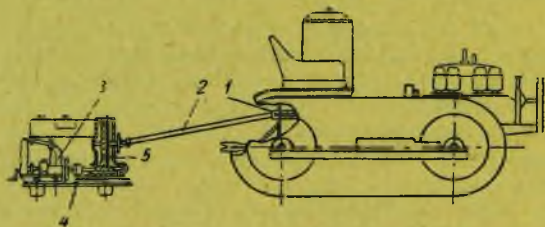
Устройство пускового приспособления ЦНИИМЭ:
